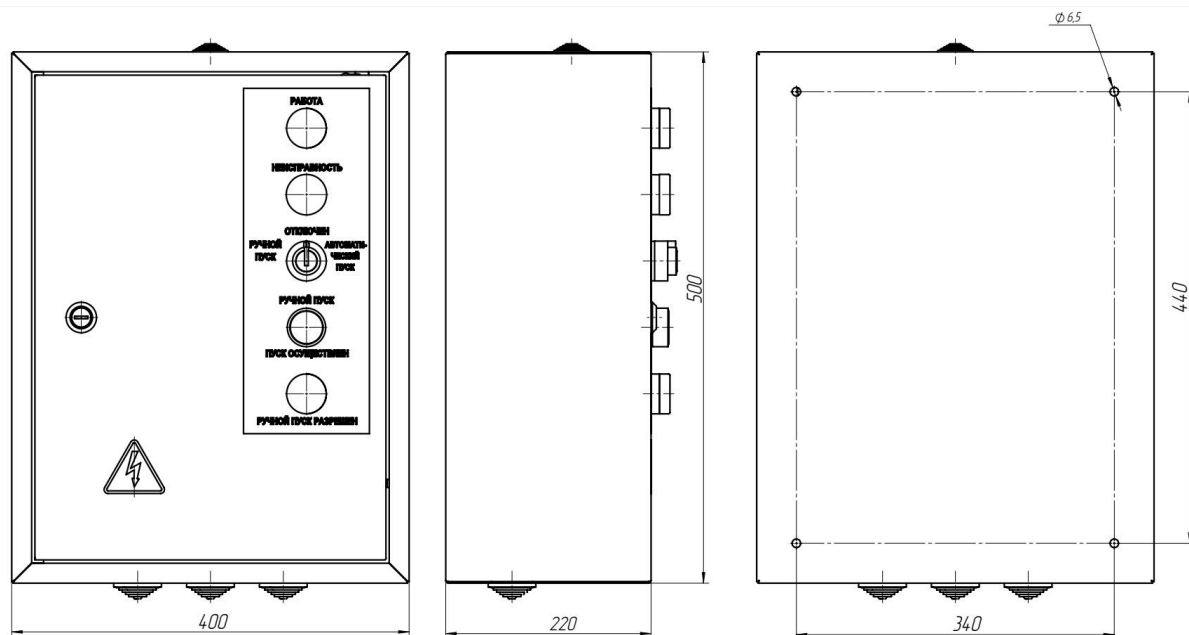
Габаритные и установочные размеры ШУП-3 исп.2К.
